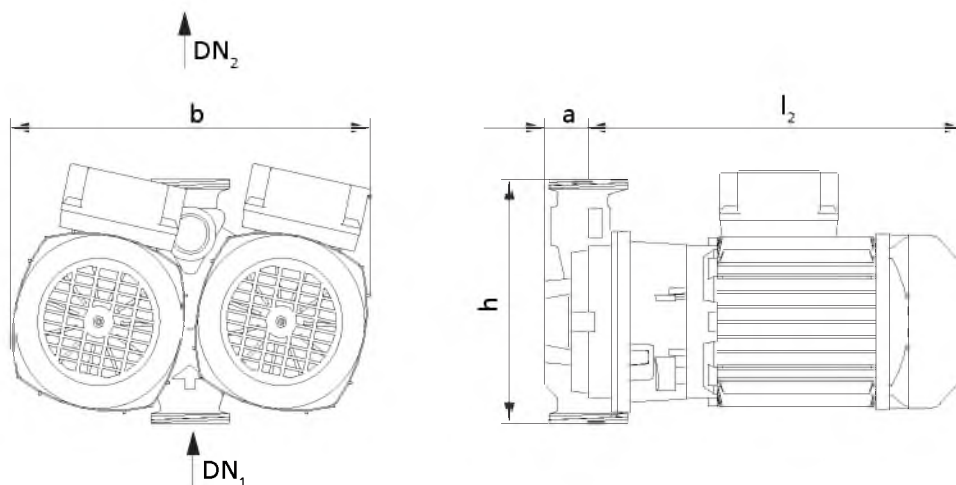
Размеры насосного агрегата с резьбовым соединением, типоразмер 032-032-080
